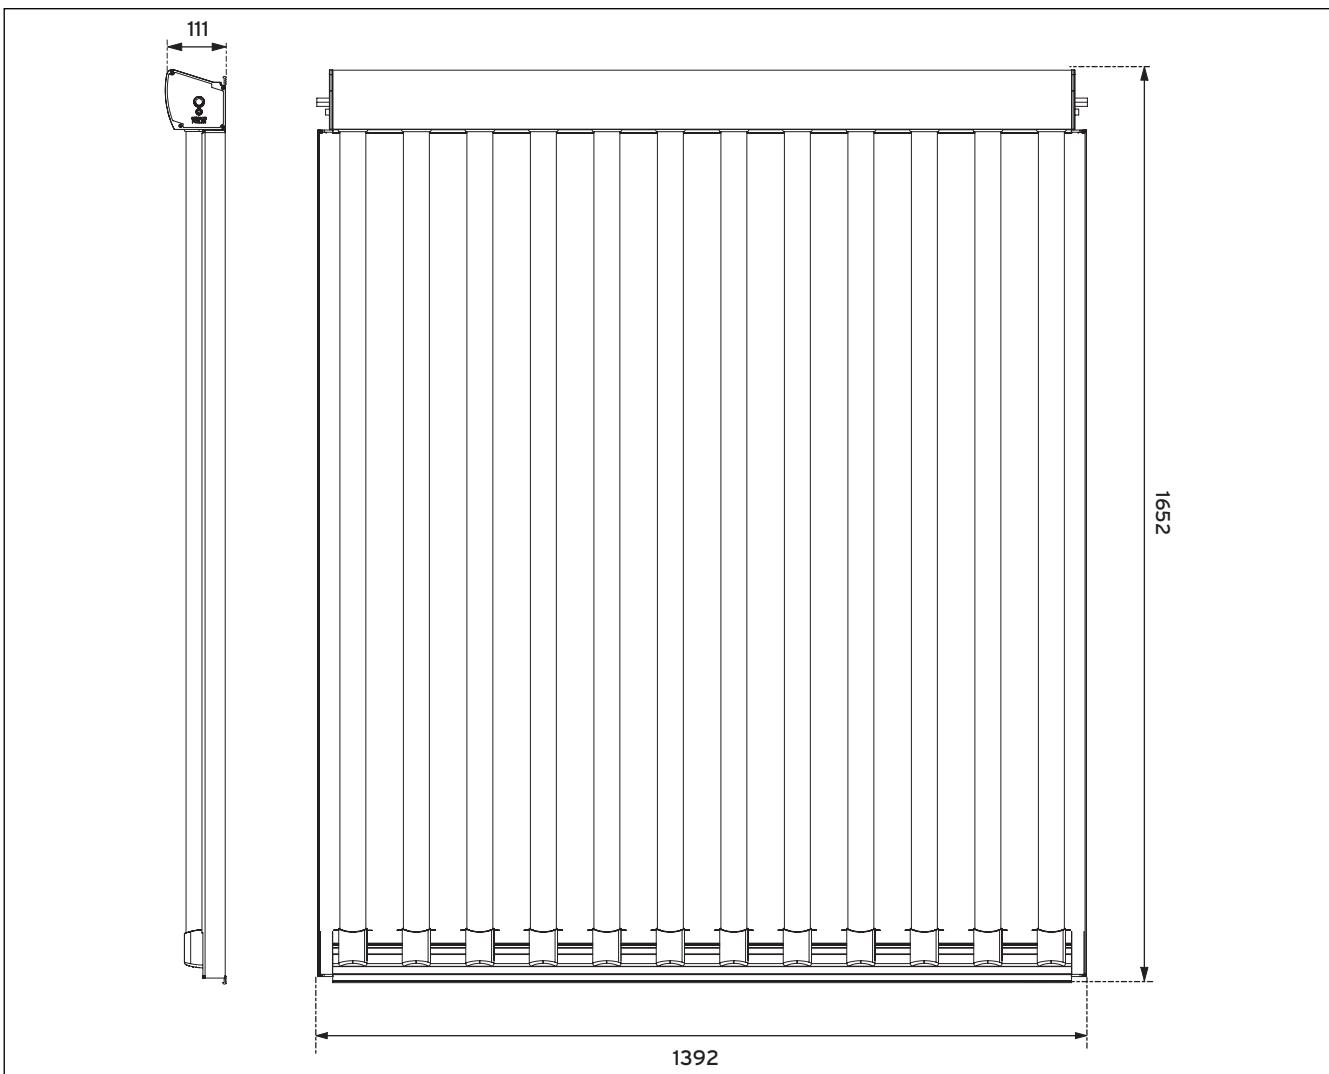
Габаритные размеры. Чертеж VTK 1140/2
